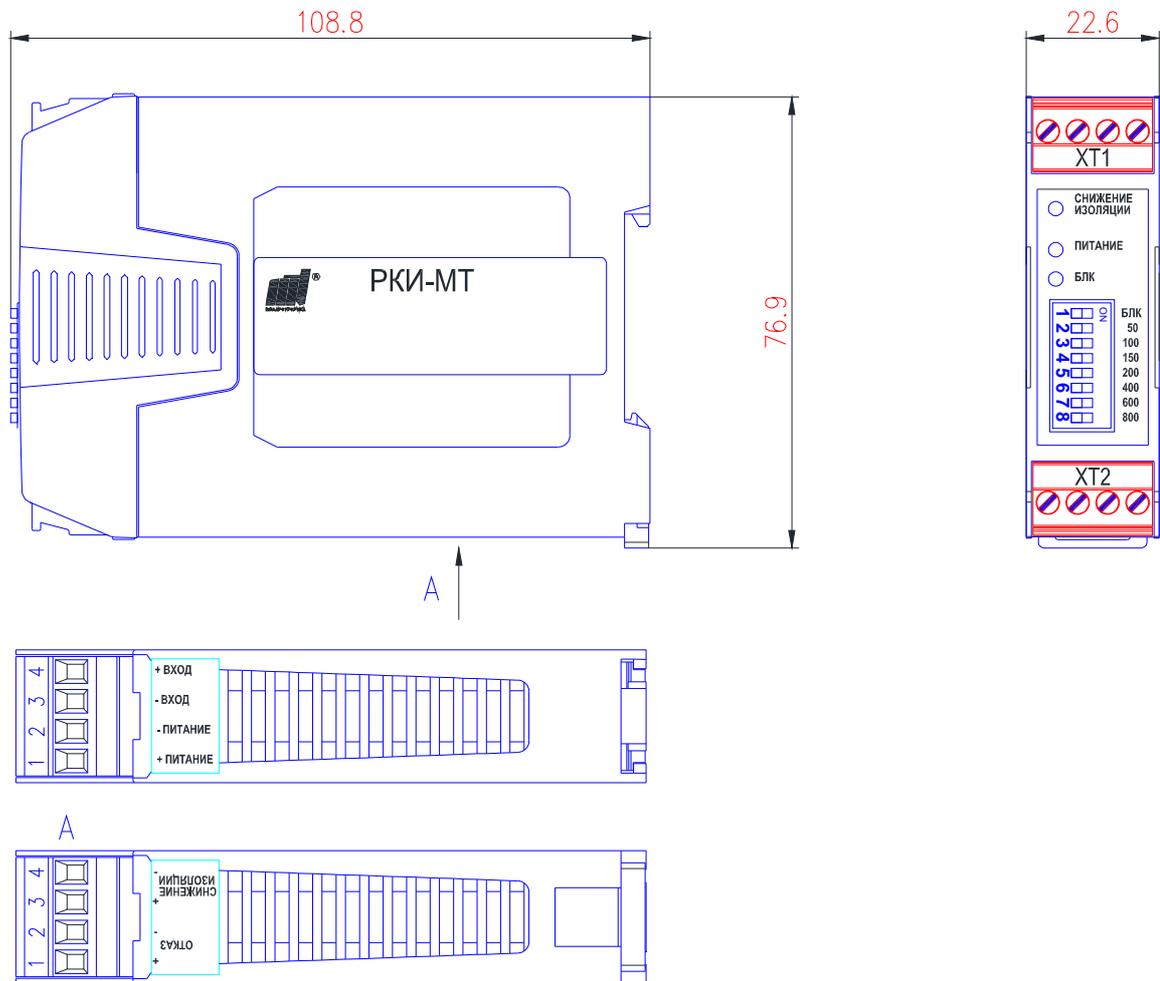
Габаритные размеры и внешний вид РКИ
